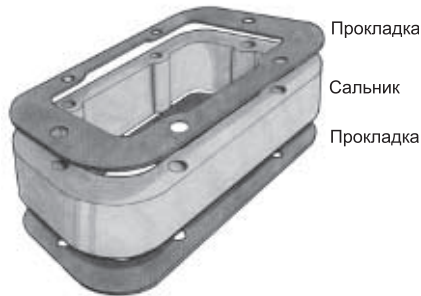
Для правильного зацепления зубчатых колес могут понадобиться блоки прокладки.
